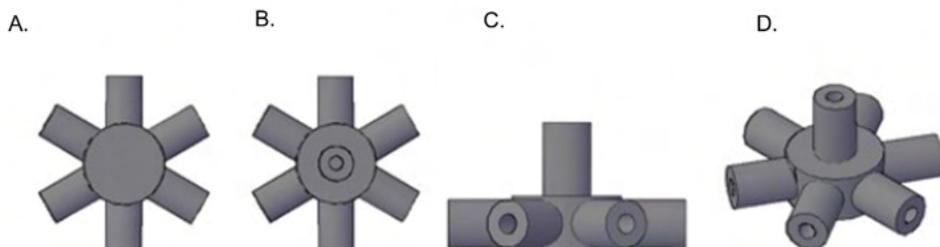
Conector: A - vista inferior; B - vista superior; C - vista lateral; D - vista em perspectiva
